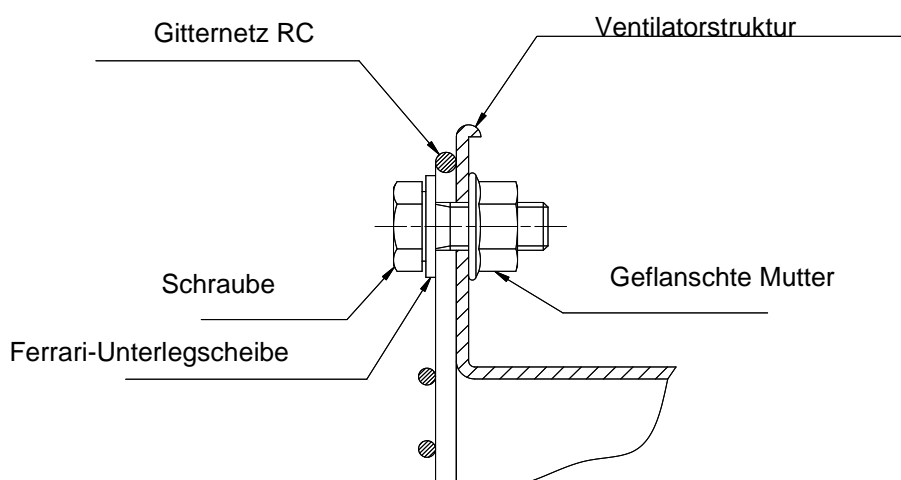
Montageplan der Schutzeinrichtung RC
